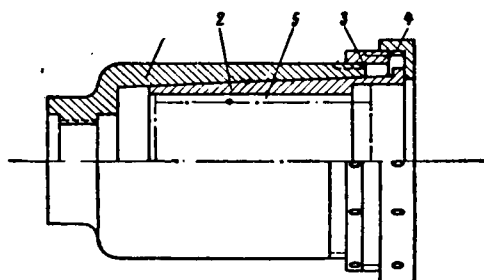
Приспособление для шлифовки втулок цилиндра по внутреннему диаметру:
